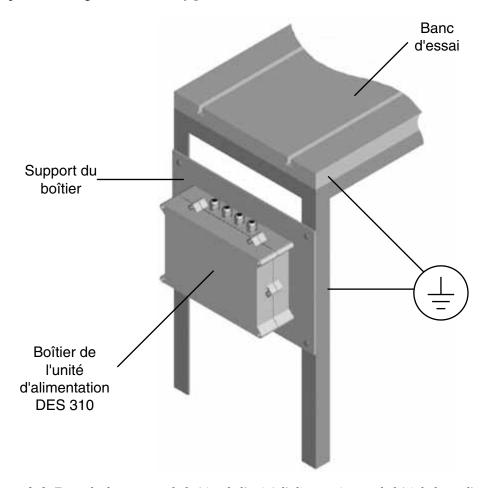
Exemple de montage du boîtier de l'unité d'alimentation sur le bâti du banc d'essai
